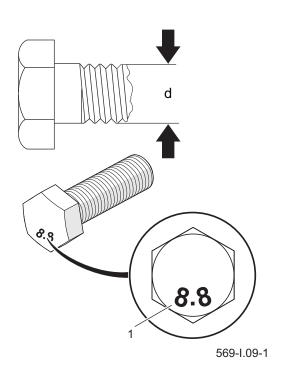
Болт с метрической резьбой (1) класс прочности (d) диаметр резьбы
